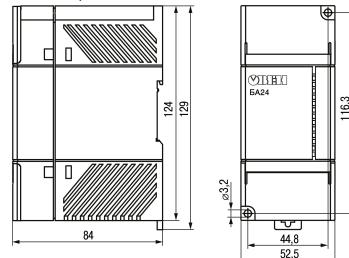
Внешний вид, габаритные и установочные размеры прибора
